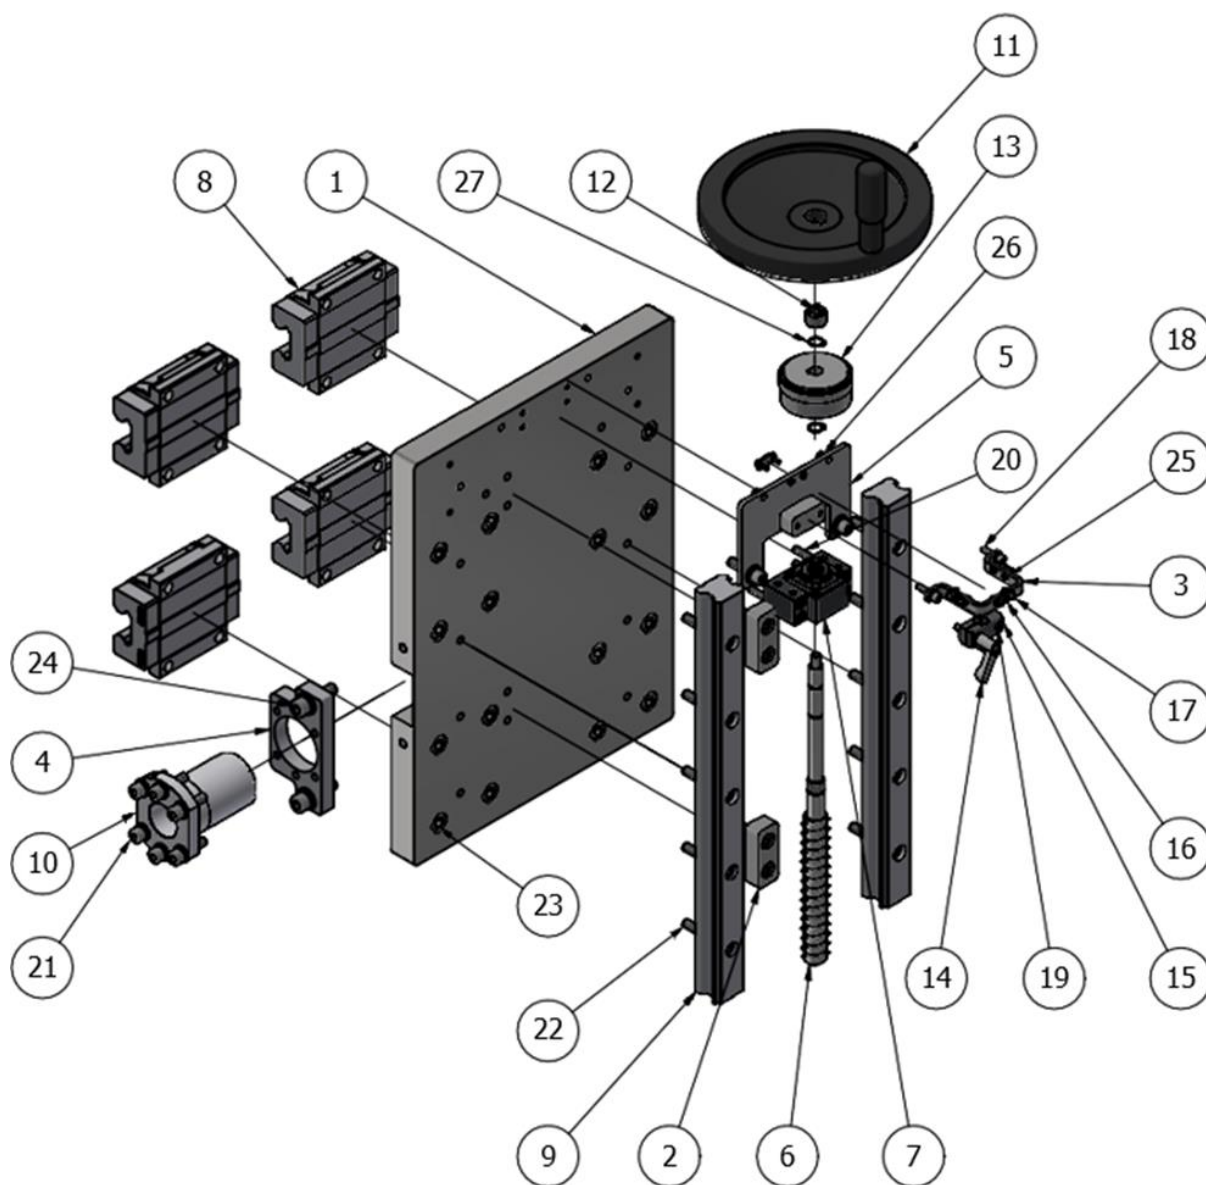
Imagem explodida da base M&G_PMM_F_V:
